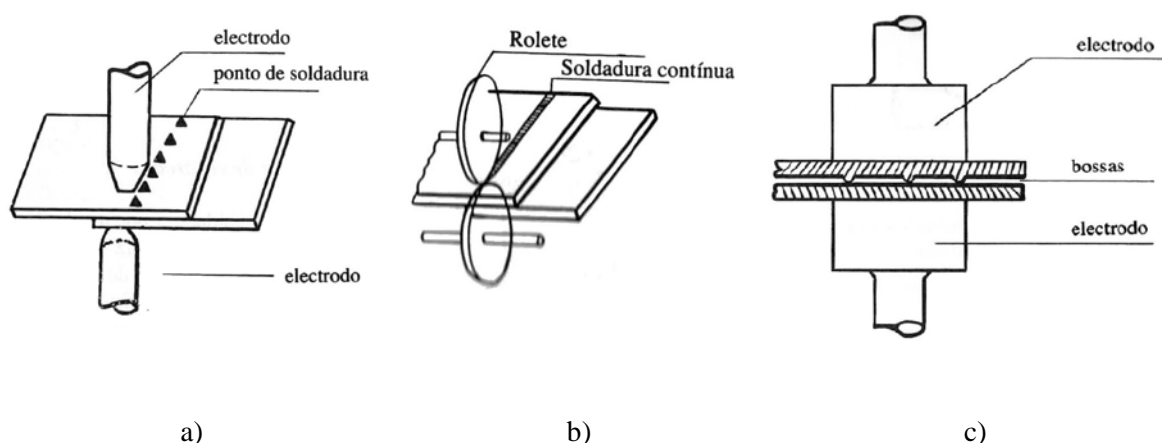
Tipos de soldadura por resistência em juntas sobrepostas [3]: a) Soldadura por pontos b) Soldadura contínua c) Soldadura por bossas
